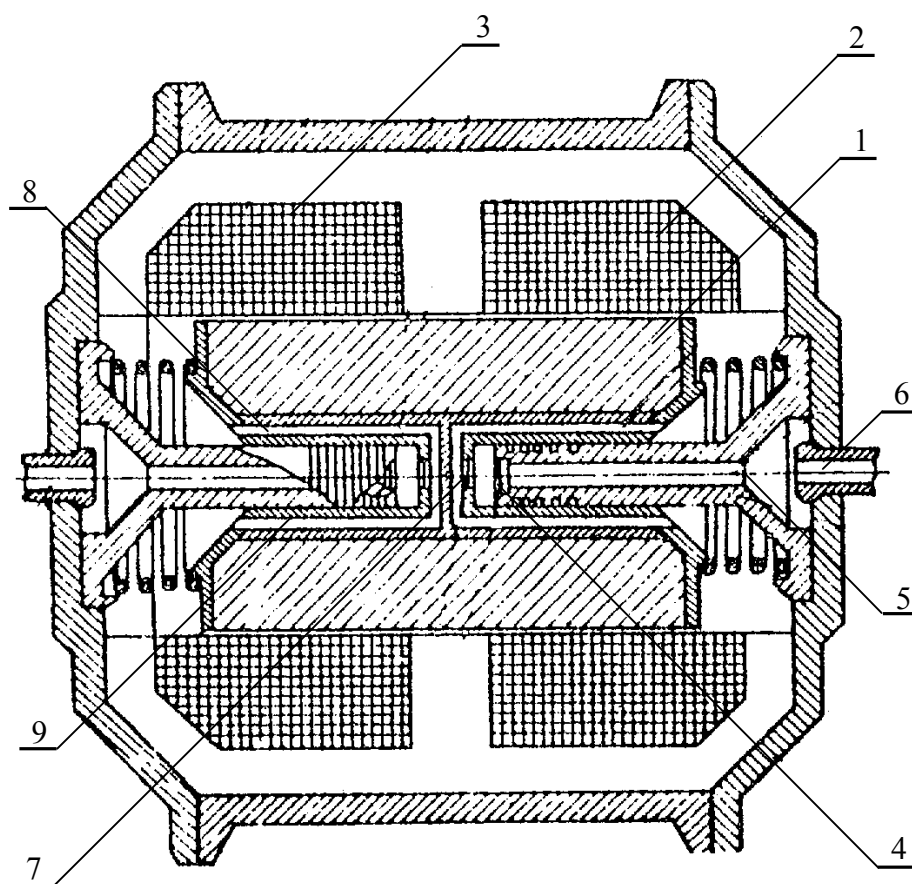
Электромагнитный компрессор с неподвижными рабочими органами
